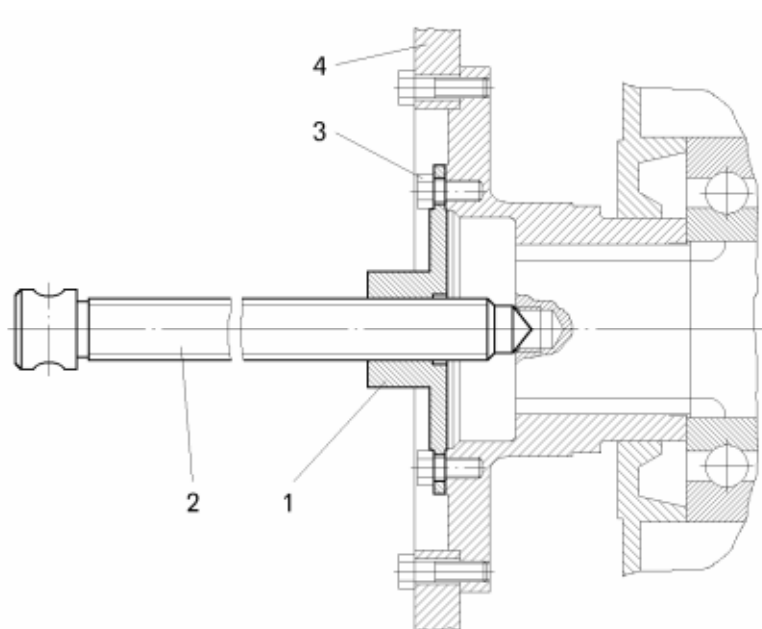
Приспособление для снятия диска тормоза с фланцем с вала тягового электродвигателя ДК-724Д:
